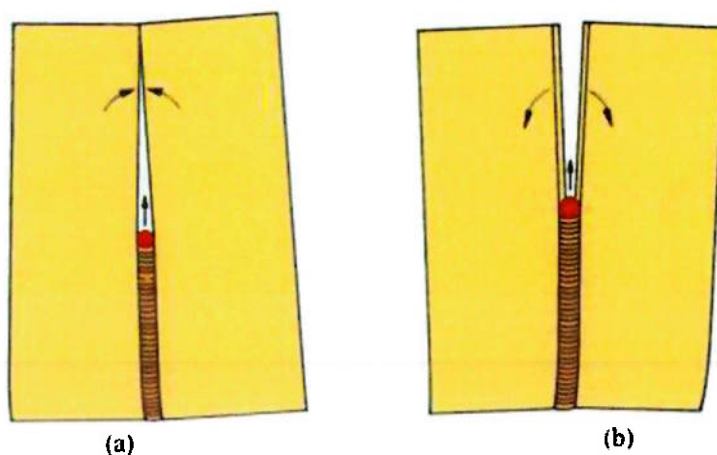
Rotação durante a soldagem para (a) Baixo e (b) Alto aporte térmico [8].
